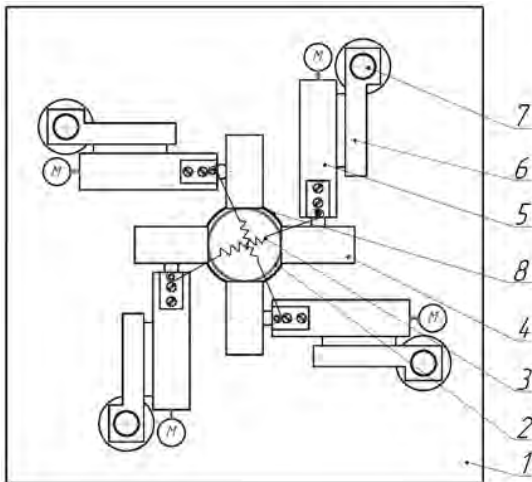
Схема механизированного приспособления для управляемого вращения шара
